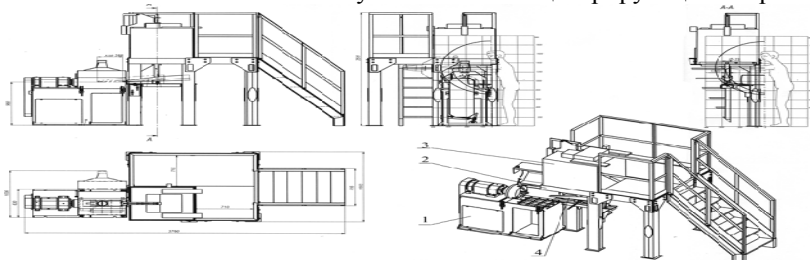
Общий вид комплекта для центробежной заливки баббитом вкладышей подшипников скольжения: 1 - «Станок СЦЗ», 2 - площадка, 3 - печь «ППН-0,6-20» или «ППН-0,6-17М», 4 – литник
